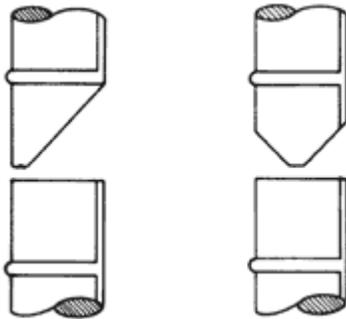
Cortes de biseles en varillas de grueso calibre que sirven para ampliar la superficie de amarre durante la soldadura.
